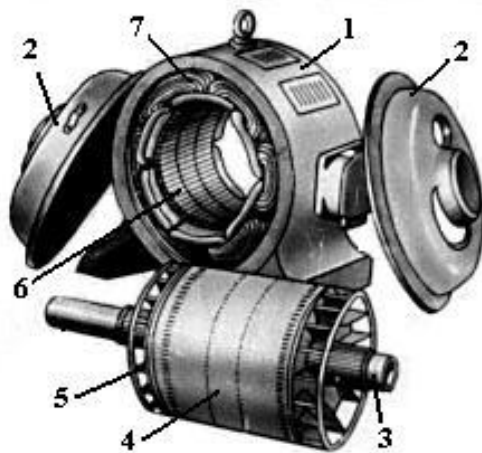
Асинхронний двигун із короткозамкненим ротором: 1 – станина, 2 – підшипникові щити, 3 – вал, 4 – осердя ротора, 5 – обмотка ротора, 6 – осердя статора, 7 – обмотка статора
